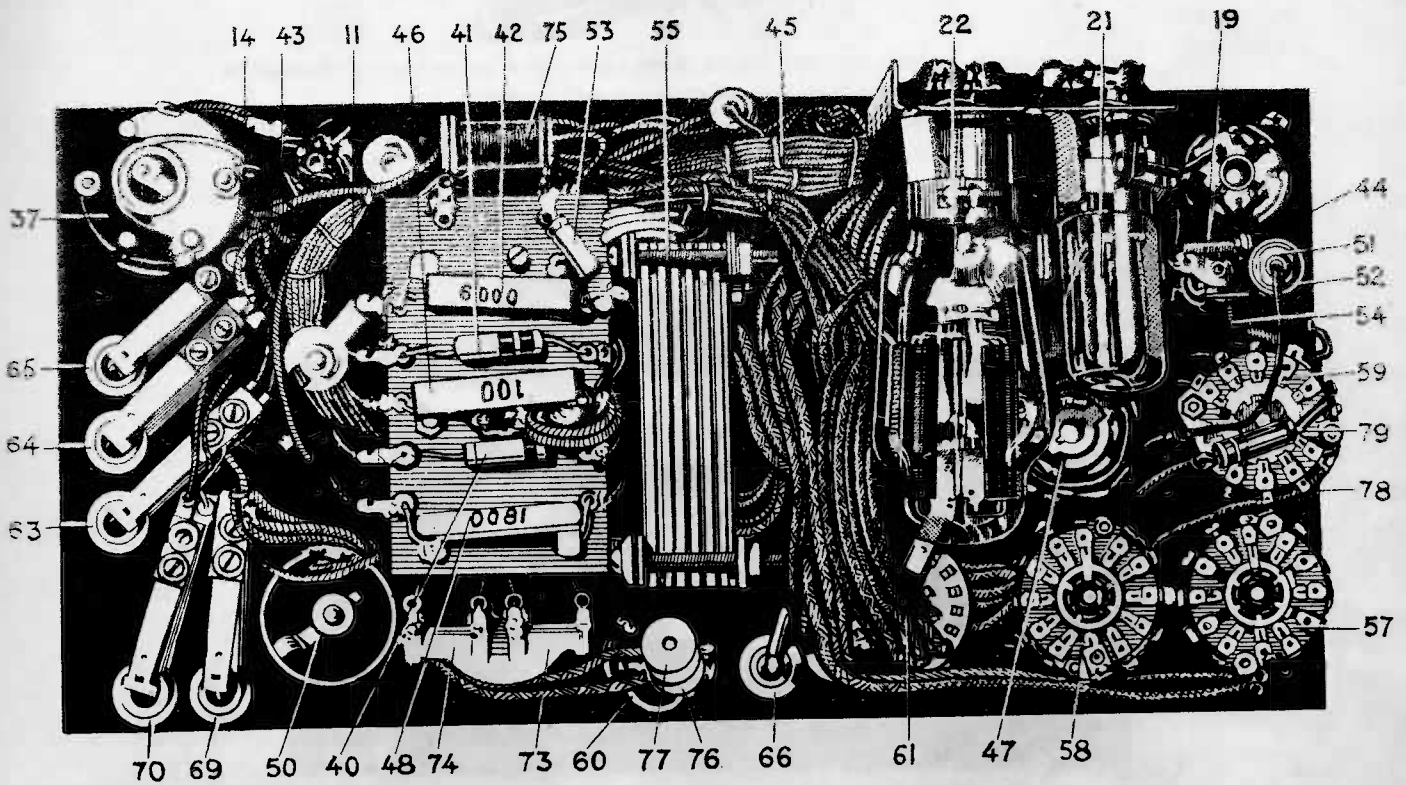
LAMPE-METRE I-177 Vue arrière du chassis
